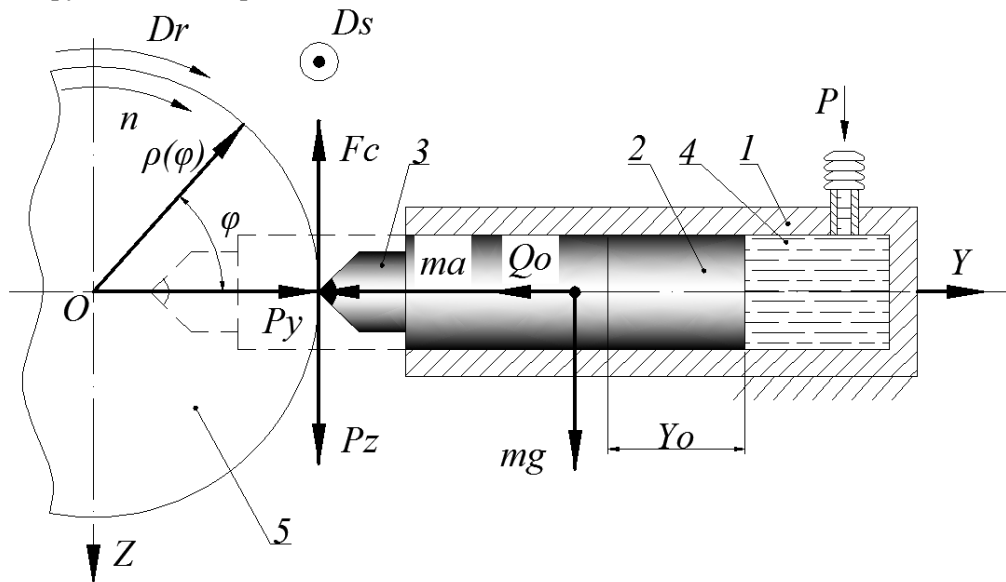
Схема вигладжування зовнішніх циліндричних поверхонь: 1 – корпус інструменту; 2 – поршень; 3 – індентор; 4 – робоча рідина; 5 – заготовка
